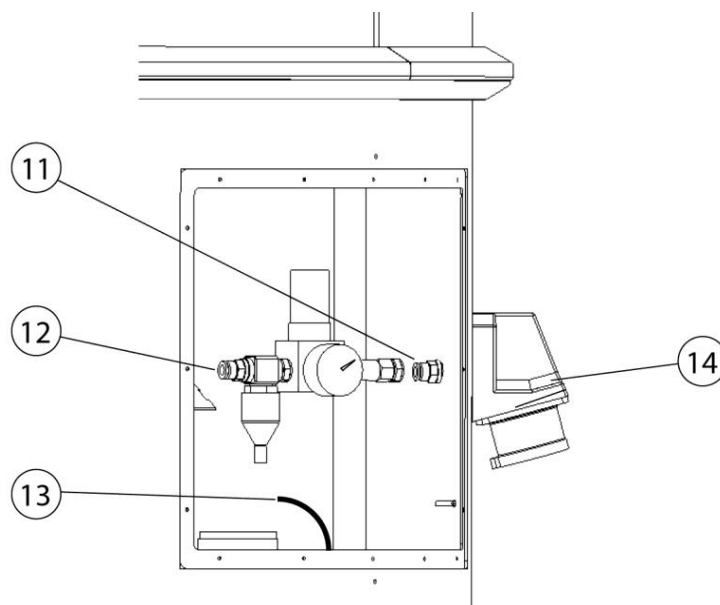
Трубопровод сжатого воздуха, дренажный трубопровод и трубопровод дифференциального давления
